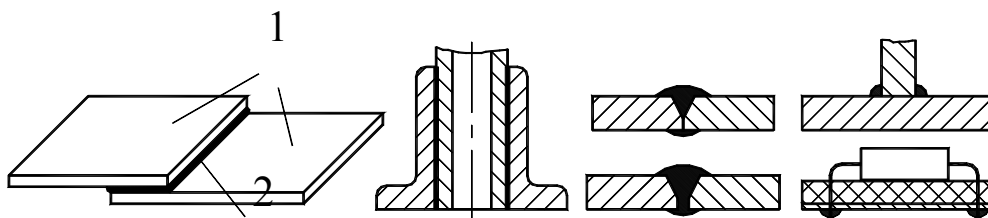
Схема пайки: 1 – заготовка, 2 - припой
